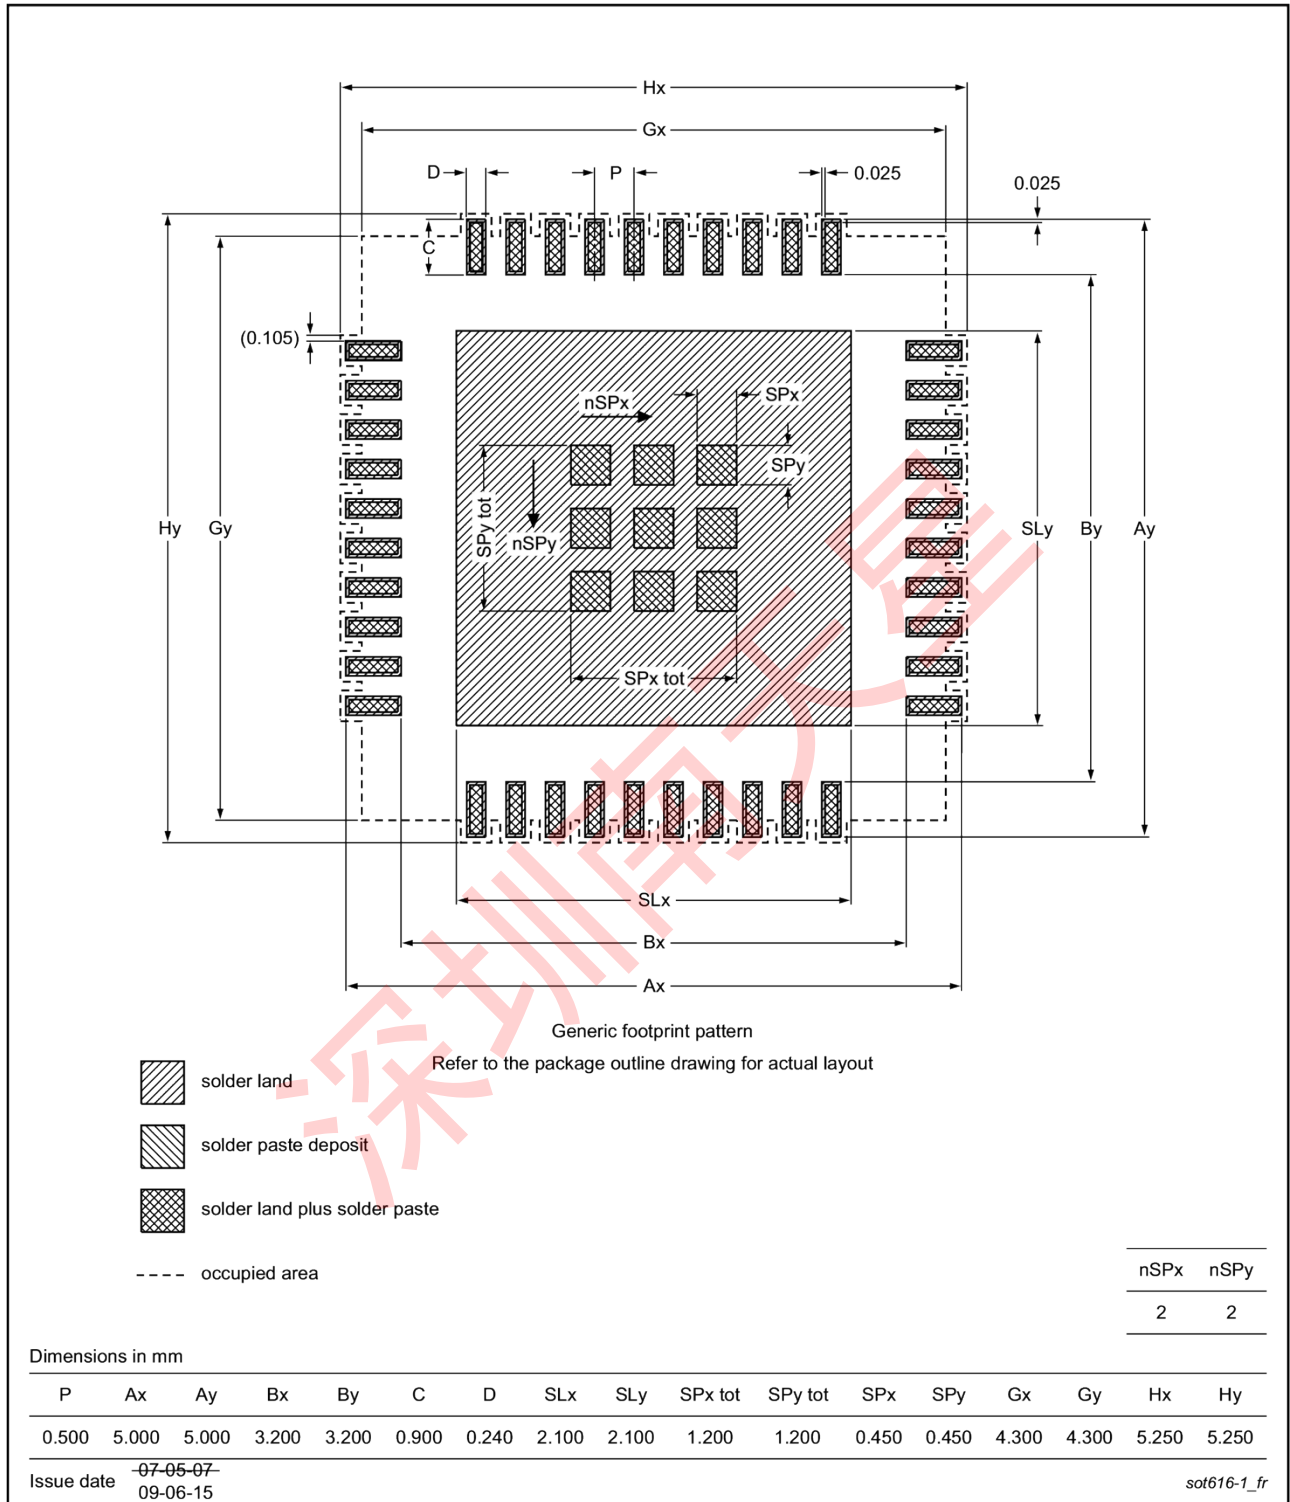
SOT616-1 (HVQFN24) 的 PCB 占地面积; 回流焊接
